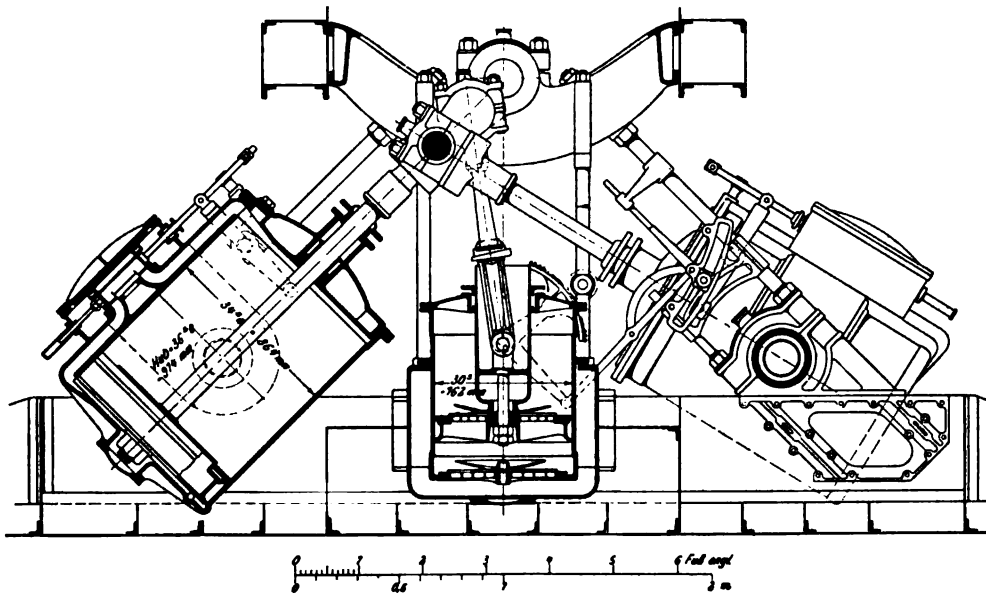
Maschine mit schwingenden Zylindern 1 : 37.
